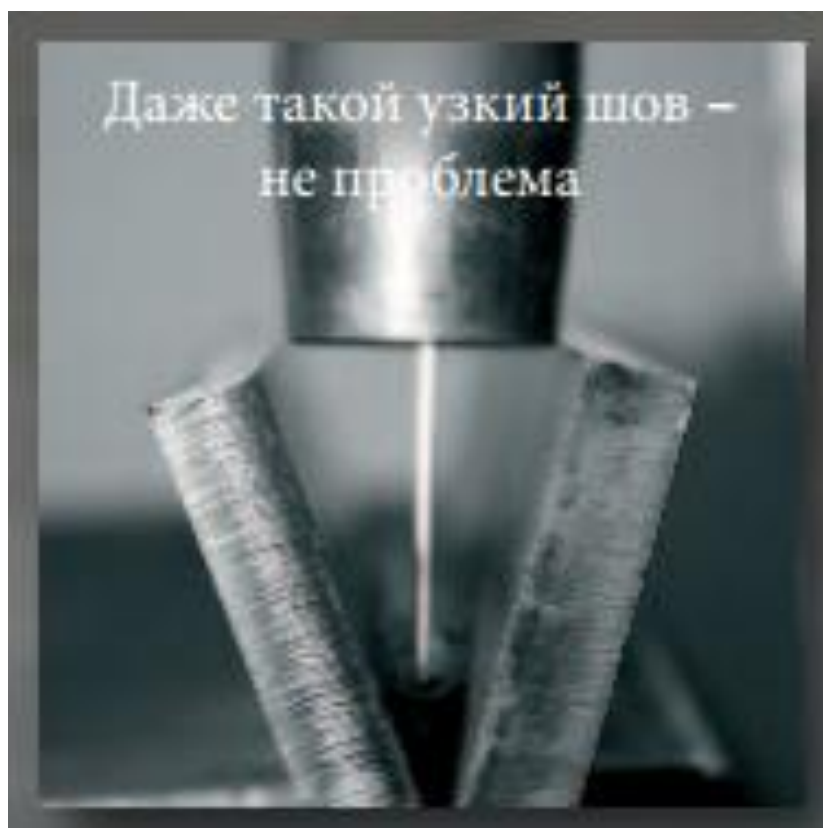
Сварка с вылетом проволоки до 40мм [4]
